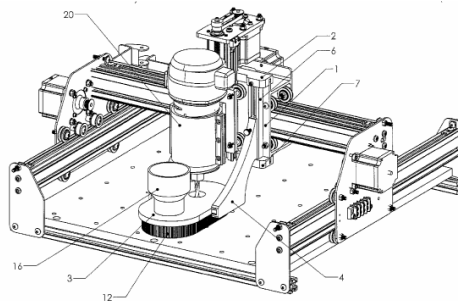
Vista Isométrica del invento acoplado a una CNC [11].
